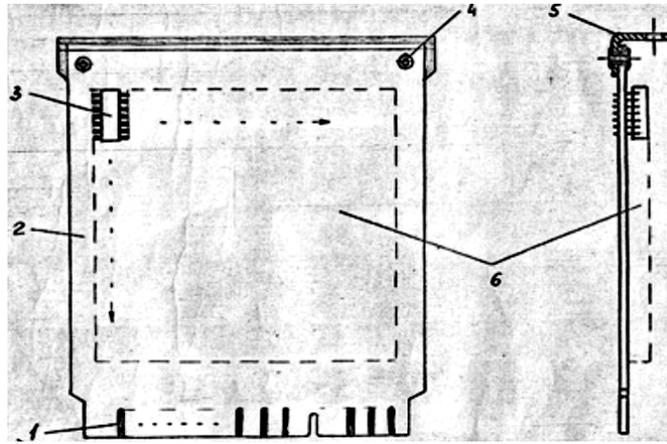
Конструкция бескорпусного типа ФЯ
